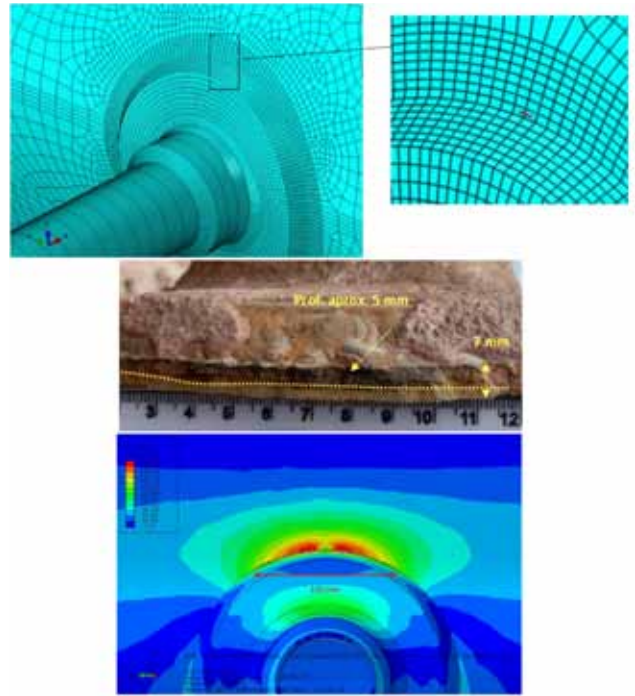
Dimensiones del defecto final: a = 5 mm, b = 125 mm
